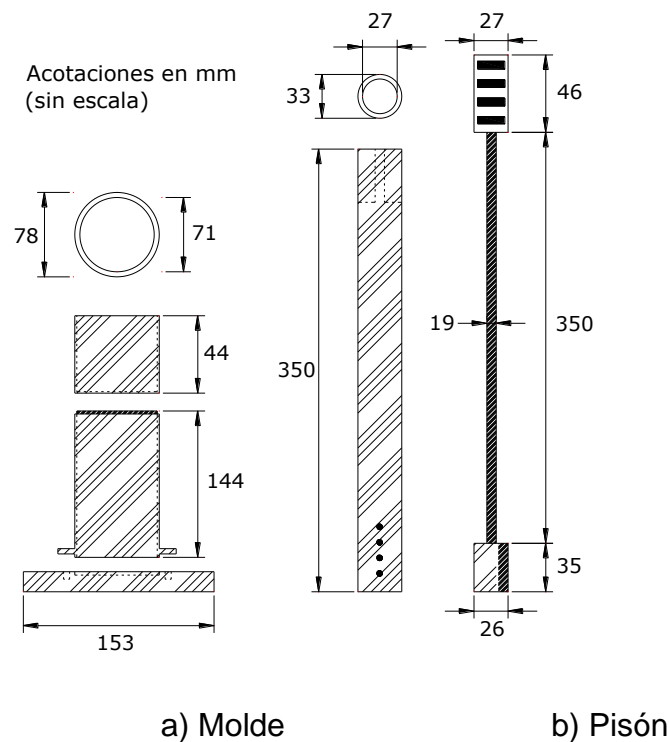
Dimensiones del molde y pisón de compactación utilizados.
